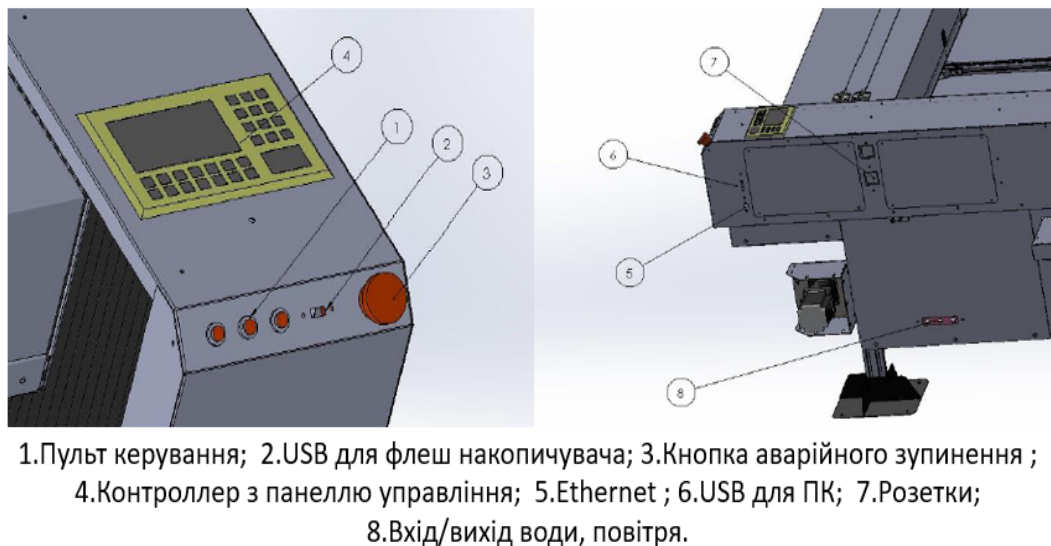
Вузли та деталі лазерного верстату [19]
